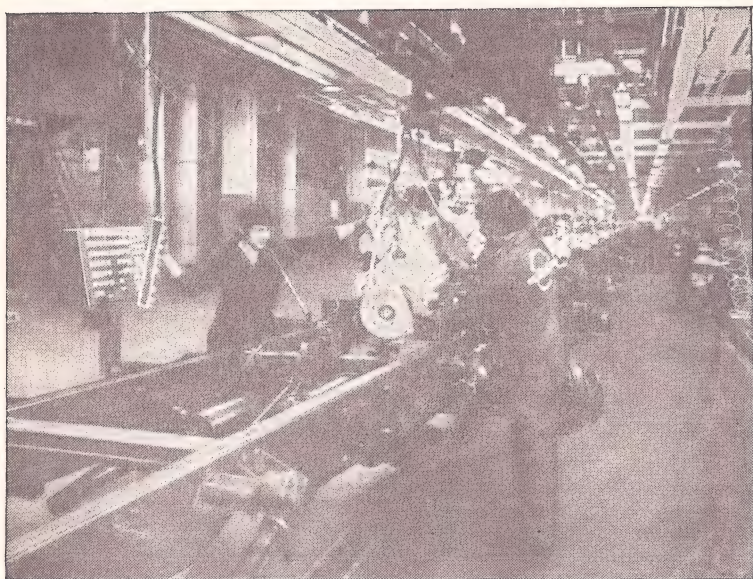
Сборочный конвейер по сборке двигателей с подвижными рабочими местами (сборка «на ходу»)
